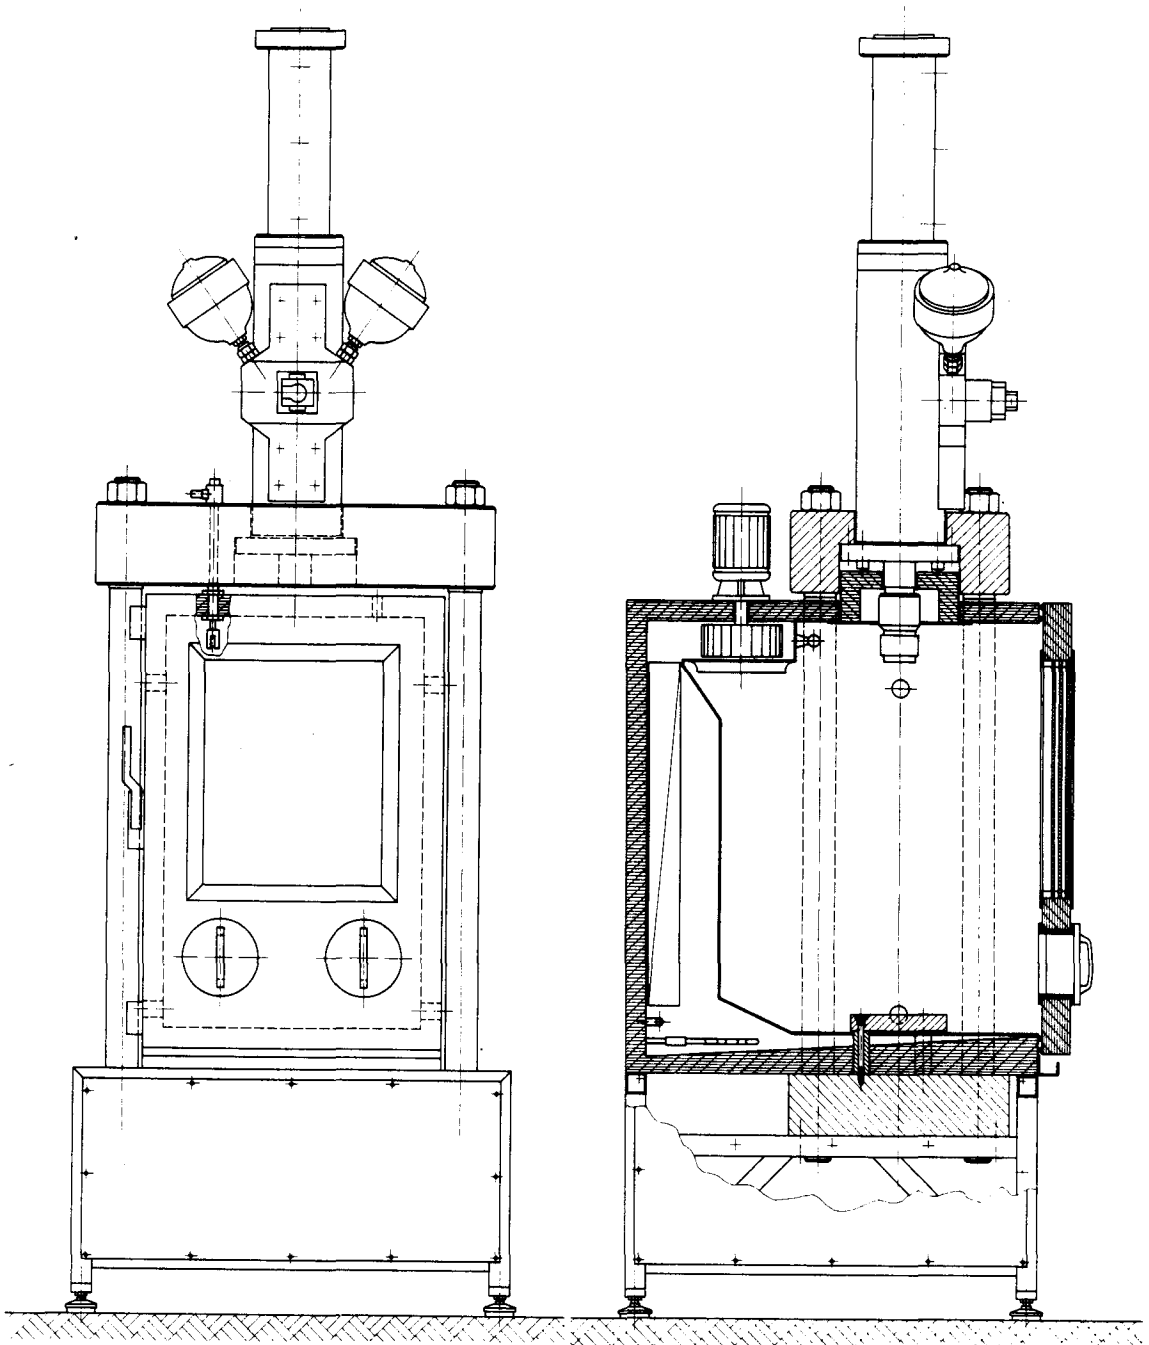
Universalprüfmaschine UVP 150 kN mit eingebauter Klimakammer. Deutlich ist der grosse freie Prüfraum mit der Basis zur Aufnahme der verschiedenen Einbauten des Baukastensystems ersichtlich.
